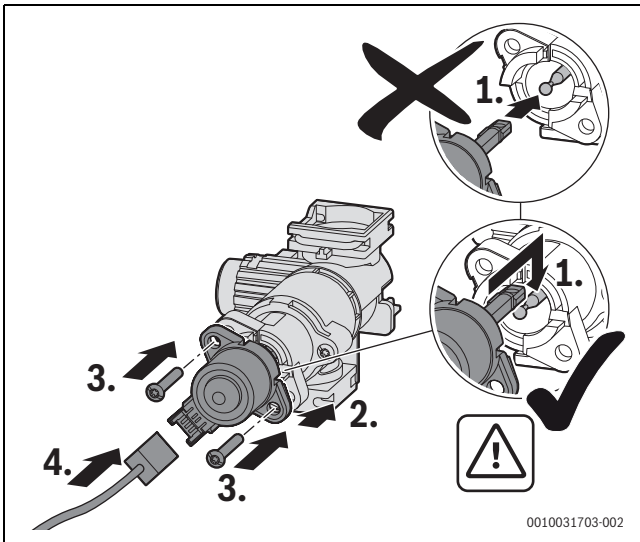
Motor am 3-Wege-Ventil einbauen (Variante mit Schrauben)
